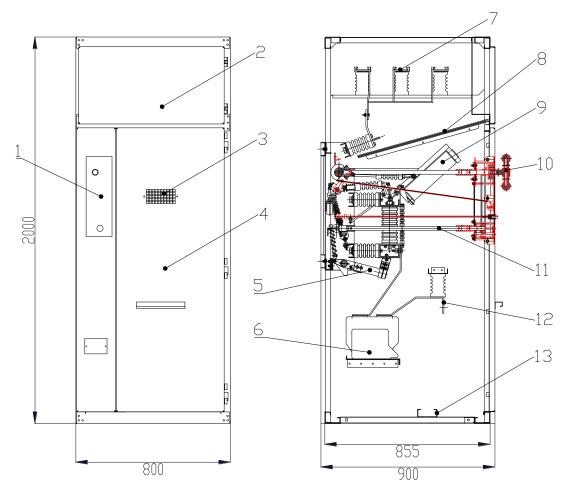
Общий вид ячейки КСО-310. 1 - панель приводов; 2 – дверь РО; 3 – смотровое окно; 4 – дверь ВО; 5 - заземлитель; 6 – трансформаторы тока; 7 – сборные шины; 8 – защитная перегородка; 9 – выключатель нагрузки; 11- привод выключателя; 12 - привод заземлителя; 13 – место подключения кабеля
